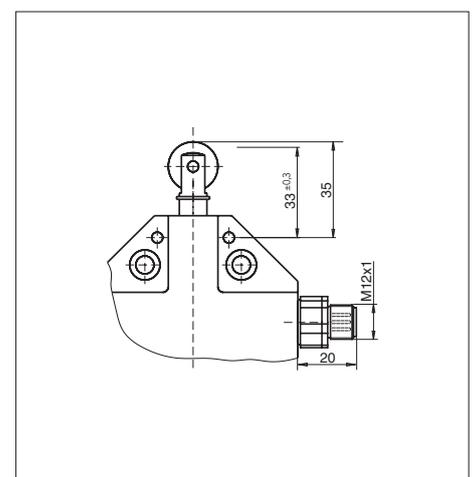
Maßzeichnung N1A... mit Steckverbinder M12
